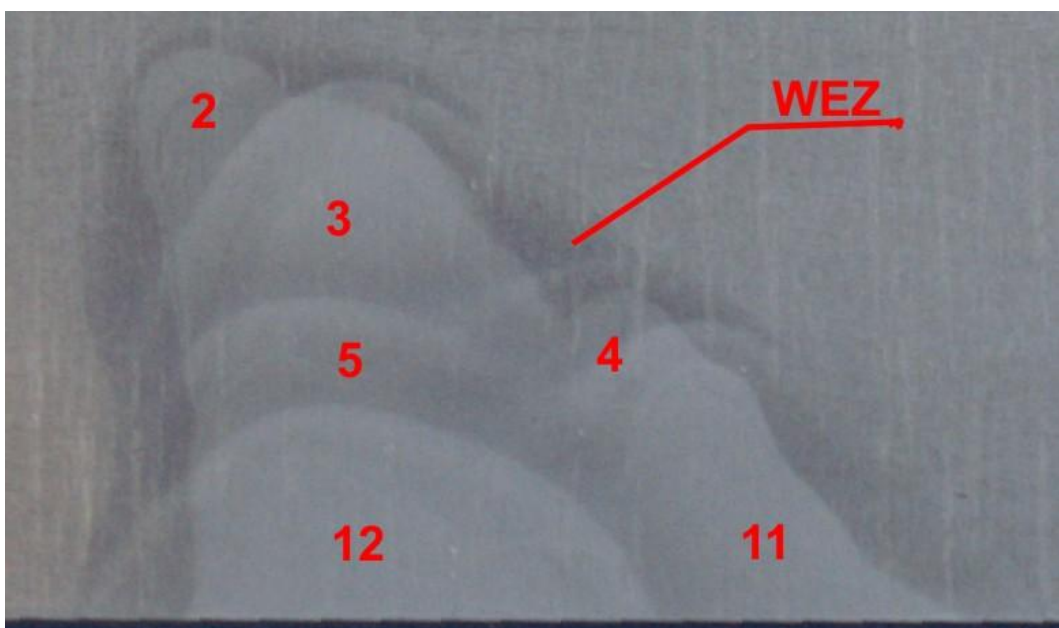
Probe 01 - Ansicht unterer Teil der Schweißnaht
